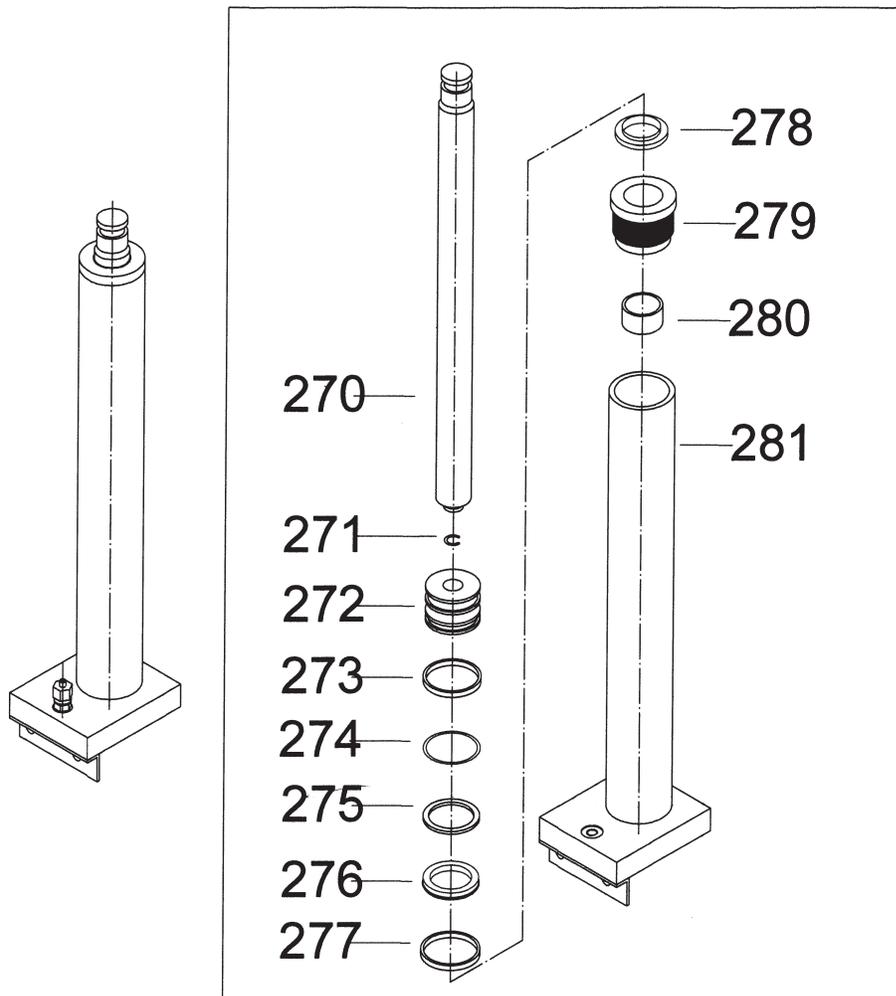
Illustration des pièces détachées pour 11K279, Unité de cylindre
